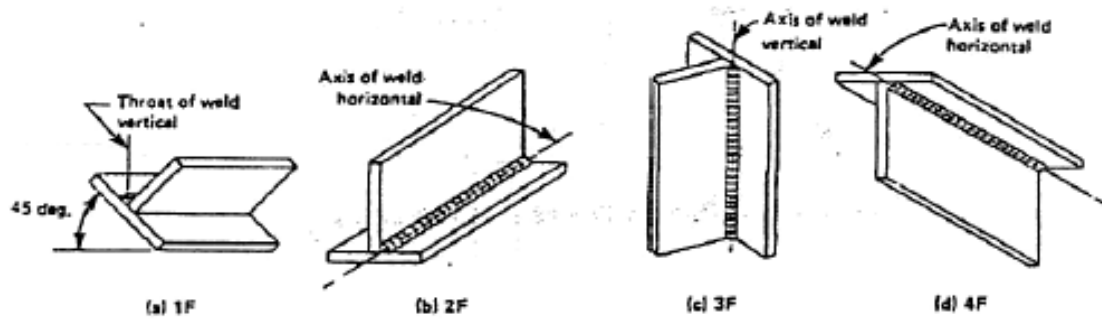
POSICIONES DE SOLDADURA EN PLACAS SON SOLDADURA DE FILETE (Ref. 5)
